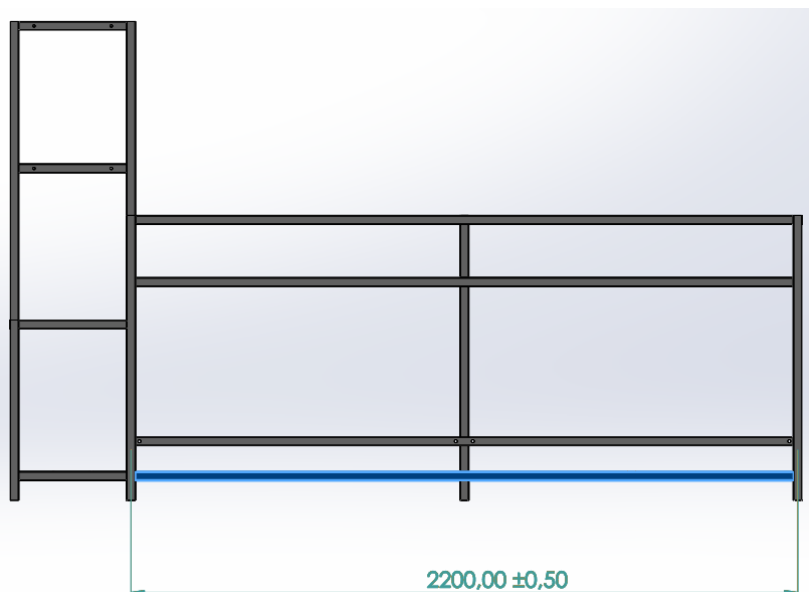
Medida del perfil seleccionado para el análisis de soldadura
